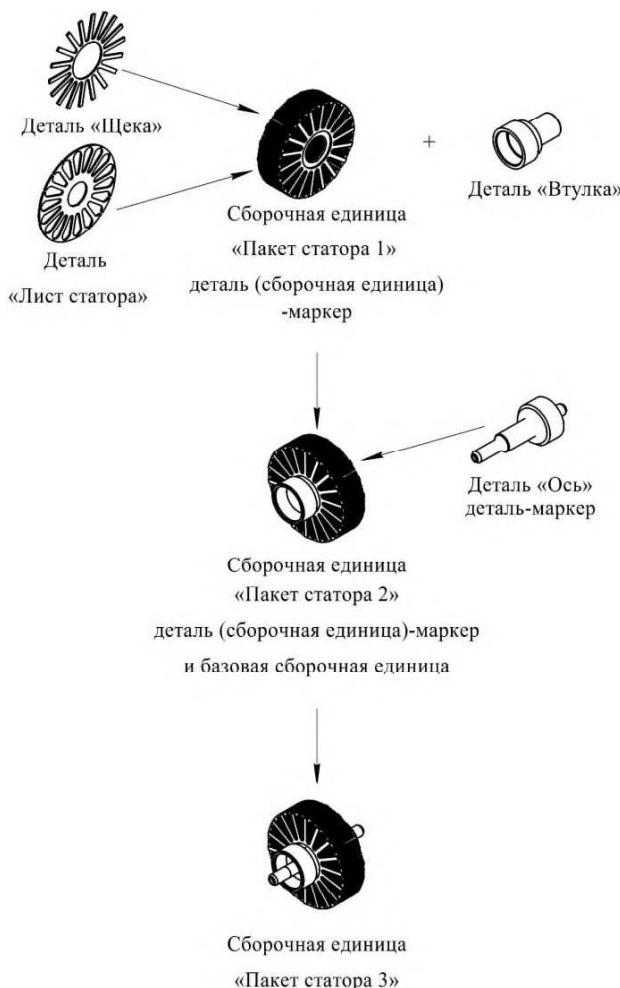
Пример разбиения сборочной единицы «Пакет статора 3», начинающегося с базовой сборочной единицы
